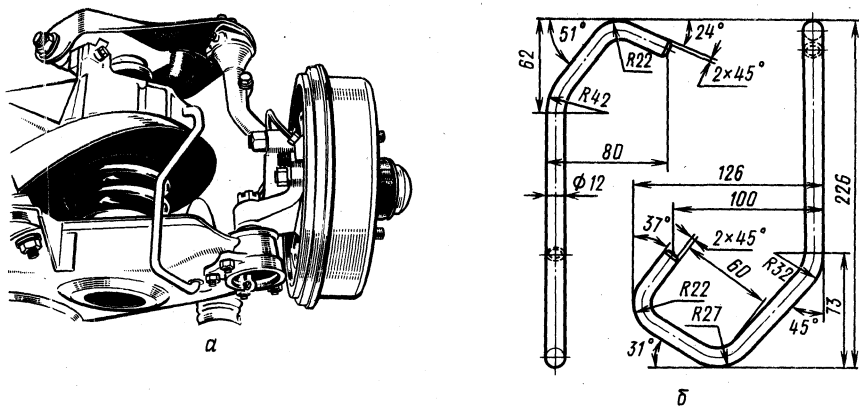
Фиксация пружины передней подвески автомобиля «Москвич»: а — установка стяжки; б — предохранительная стяжка
